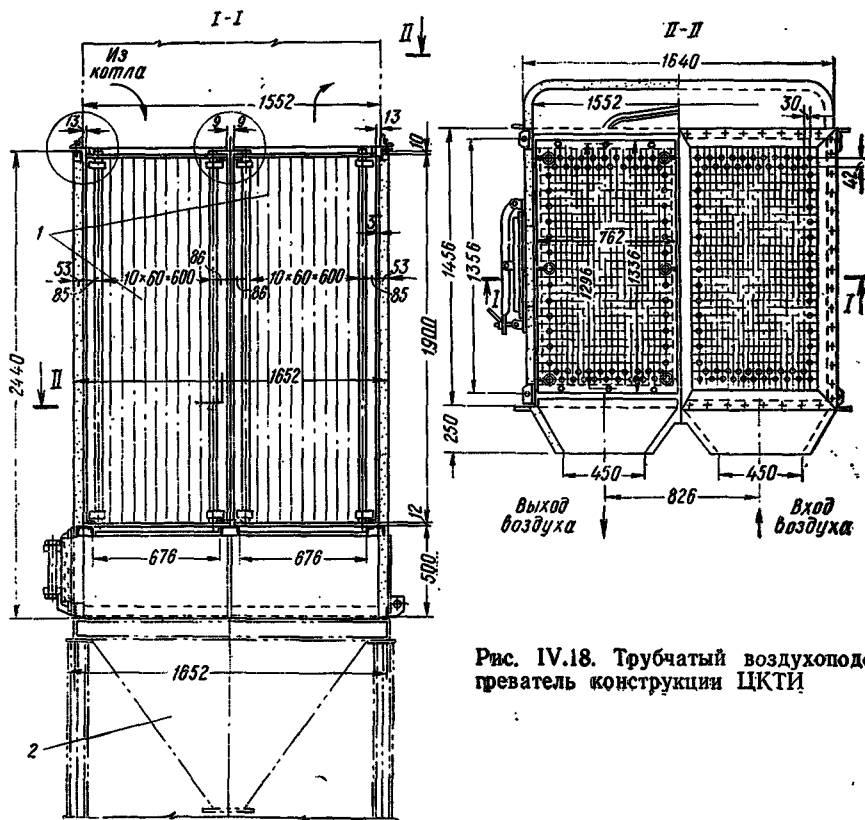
Трубчатый воздухоподогреватель конструкции ЦКТИ
